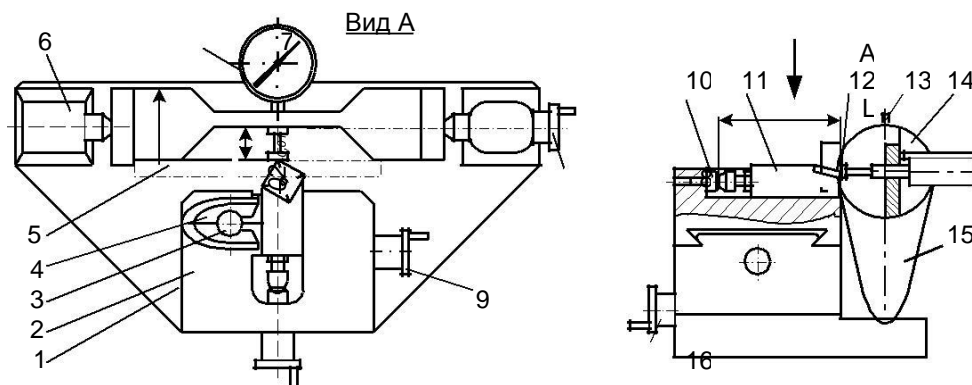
Схема индикаторного приспособления для исследования точности позиционирования резца: 1 - плита; 2 - резцедержавка; 3 - винт; 4 - клин; 5 - планка; 6 - центровая бабка; 7 - индикатор; 8 - рукоятка; 9 - рукоятка продольного перемещения; 10 - упор; 11 - резцовая вставка; 12 - вершина резца; 13 - рукоятка противовеса; 14 - оправка; 15 - противовес; 16 - рукоятка поперечного перемещения
